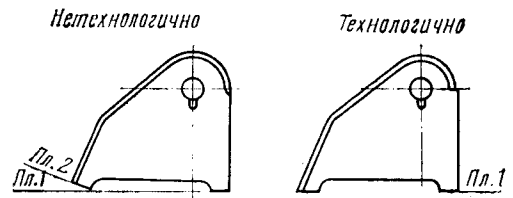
Расположение поверхностей под стыковую сварку.
